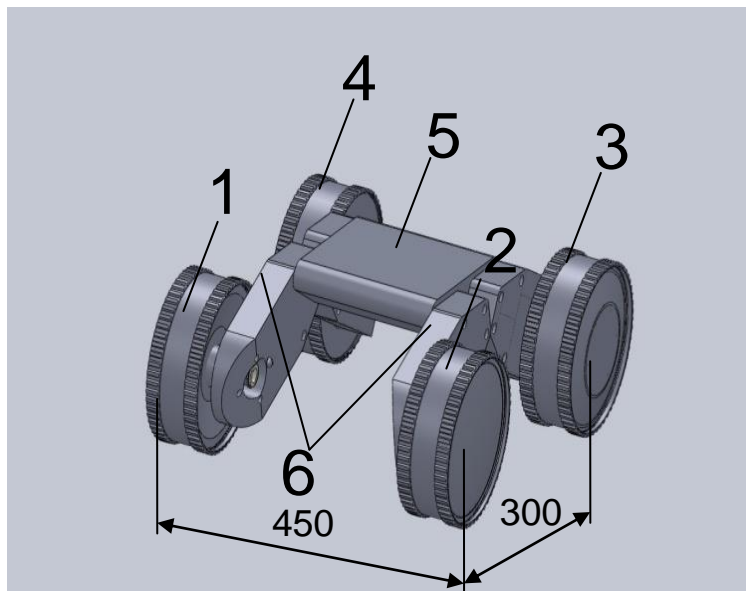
Общий вид шасси мобильного робота (1, 2 – приводные модули; 3, 4 –неприводные модули; 5 – платформа крепления оборудования; 6 – корпуса расположения плат системы управления и аккумуляторов)
